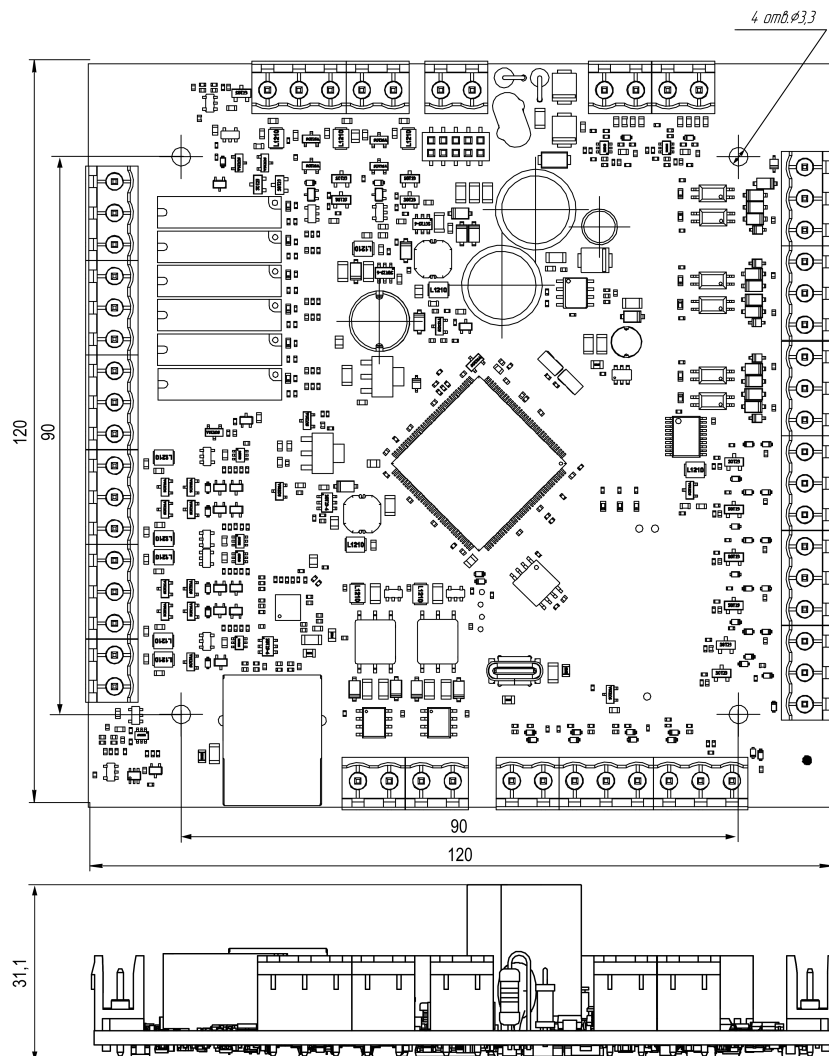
Габаритные и установочные размеры ОВК-П-24
